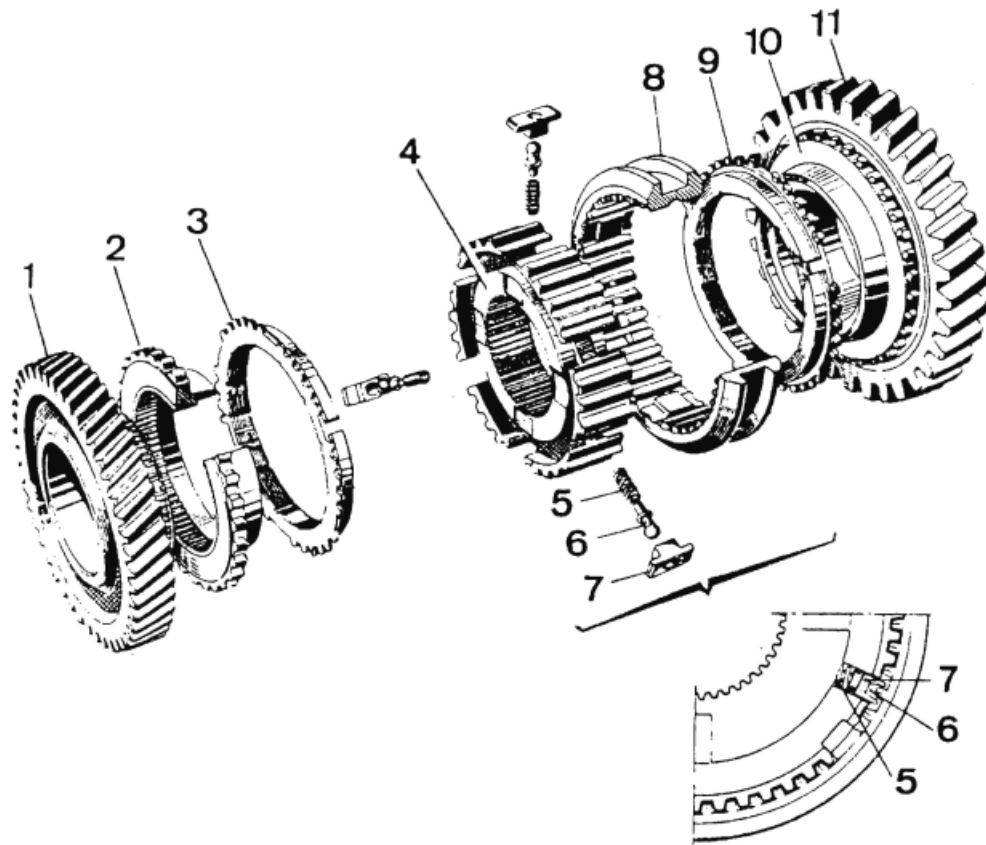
Розгорнутий вигляд синхронізатора 1-ї/2-ї передач:
